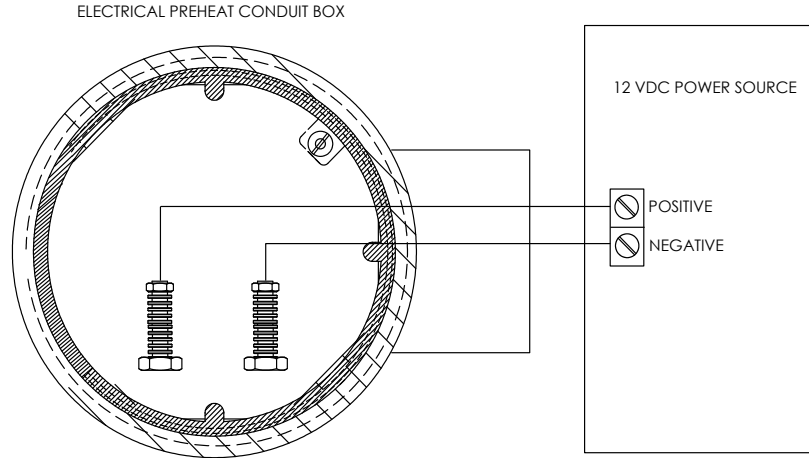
Instruções de instalação elétrica do pré-aquecedor elétrico
